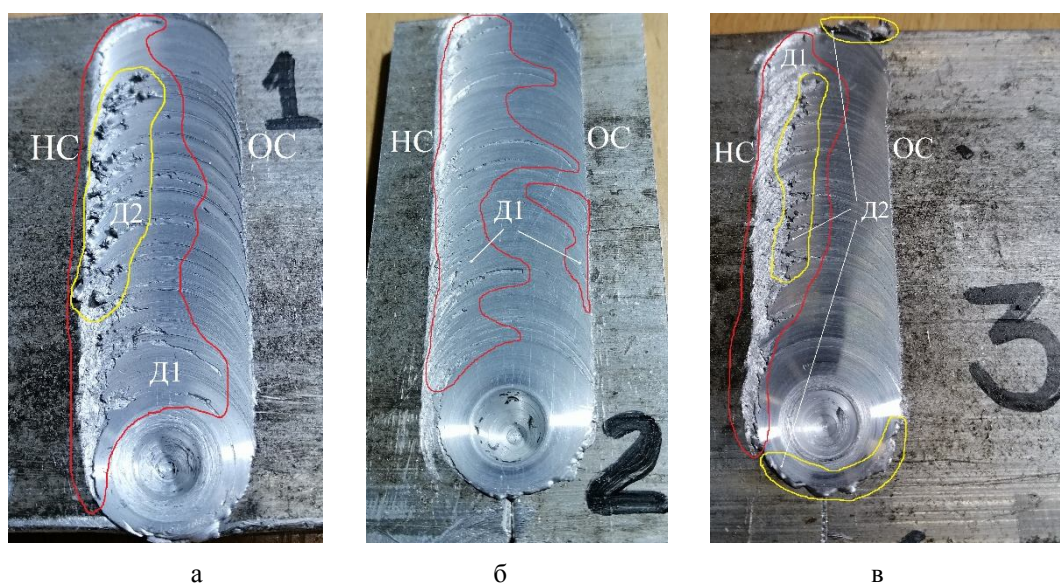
Общий вид полученных сварных соединений
